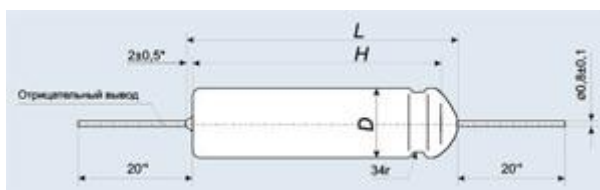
Габаритный чертеж корпуса оксидно-электрического алюминиевого конденсатора К50-29 (тип 1).
